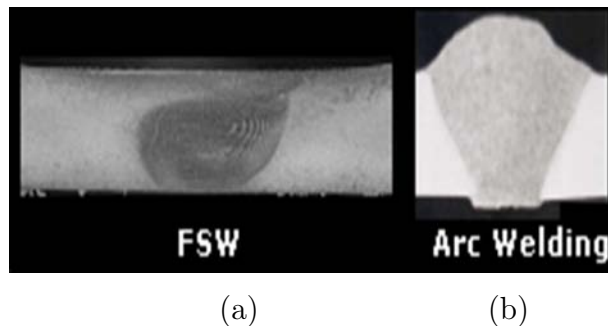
(a)- Coupe transversale d'une soudure par FSW. (b)- Coupe transversale d'une soudure à l'arc.
